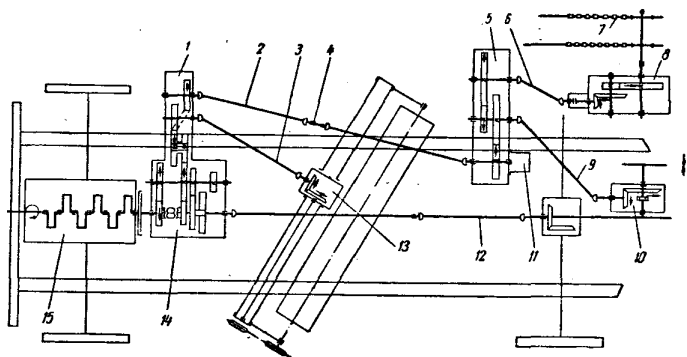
Кинематическая схема пескоразбрасывателя ПР-53
